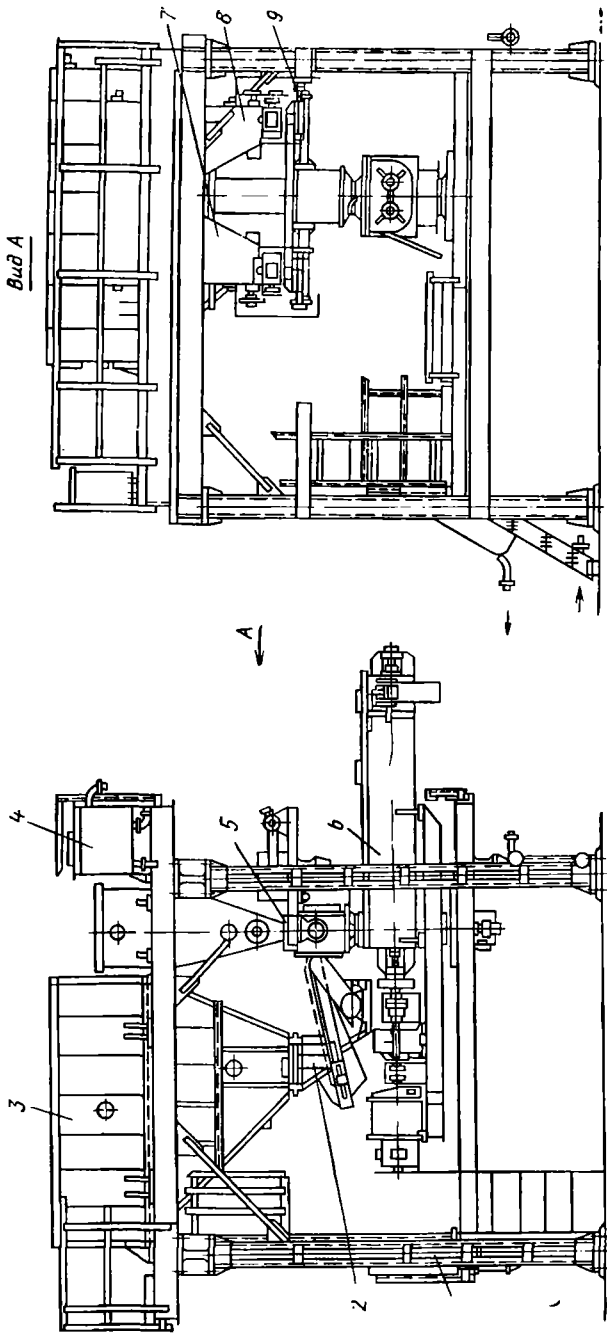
Установка непрерывного действия для приготовления жидких смесей
